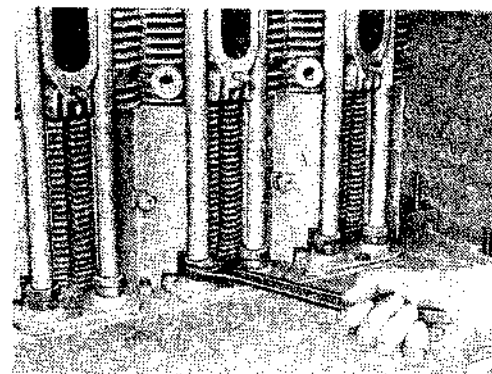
Sechskantschrauben der Einspritzpumpen-Kupplung nachziehen
